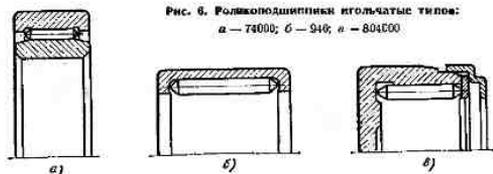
Роликоподшипники игольчатые типов: а — 74000; б — 940; в — 804000
